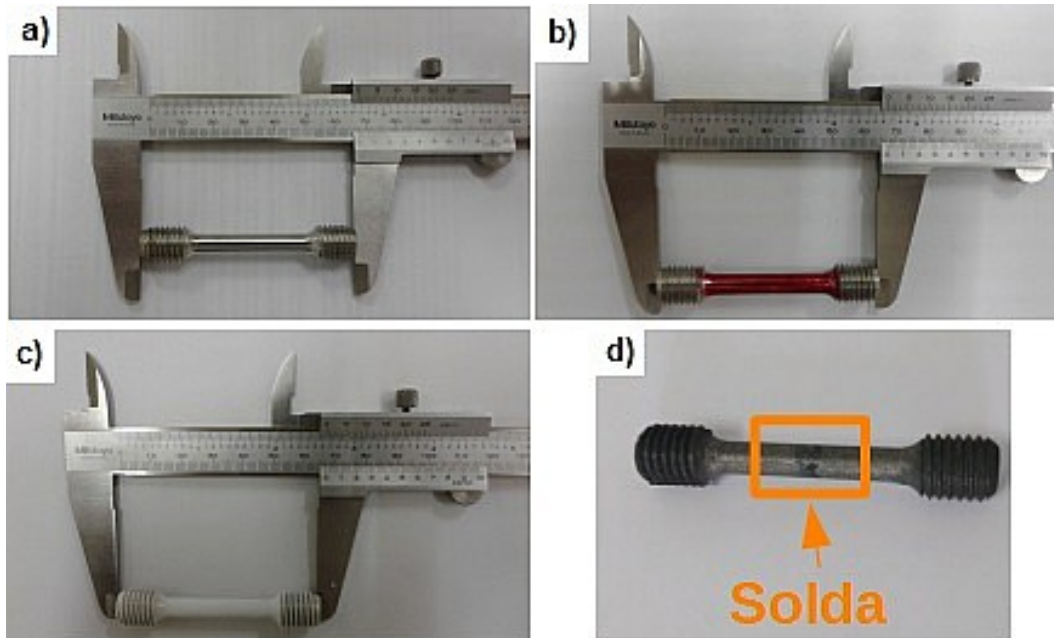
Ensaio de líquido penetrante e envelhecimento do corpo de prova. a) Corpo de prova usinado. b) Aplicação do líquido penetrante. c) aplicação do revelador. d) Corpo de prova da junta soldada após envelhecimento, com destaque para o cordão de solda.
